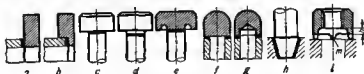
Uniones de soldadura eléctrica por contacto
